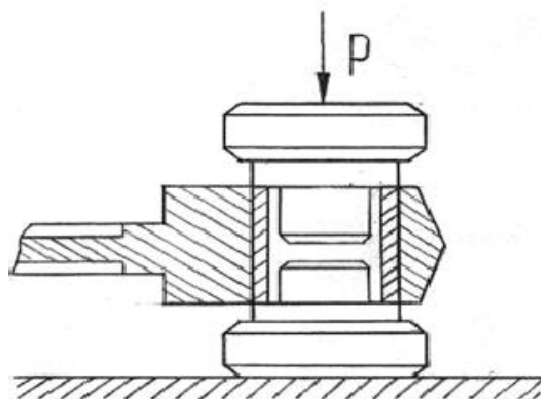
Восстановление втулок осадкой без выпрессовки
